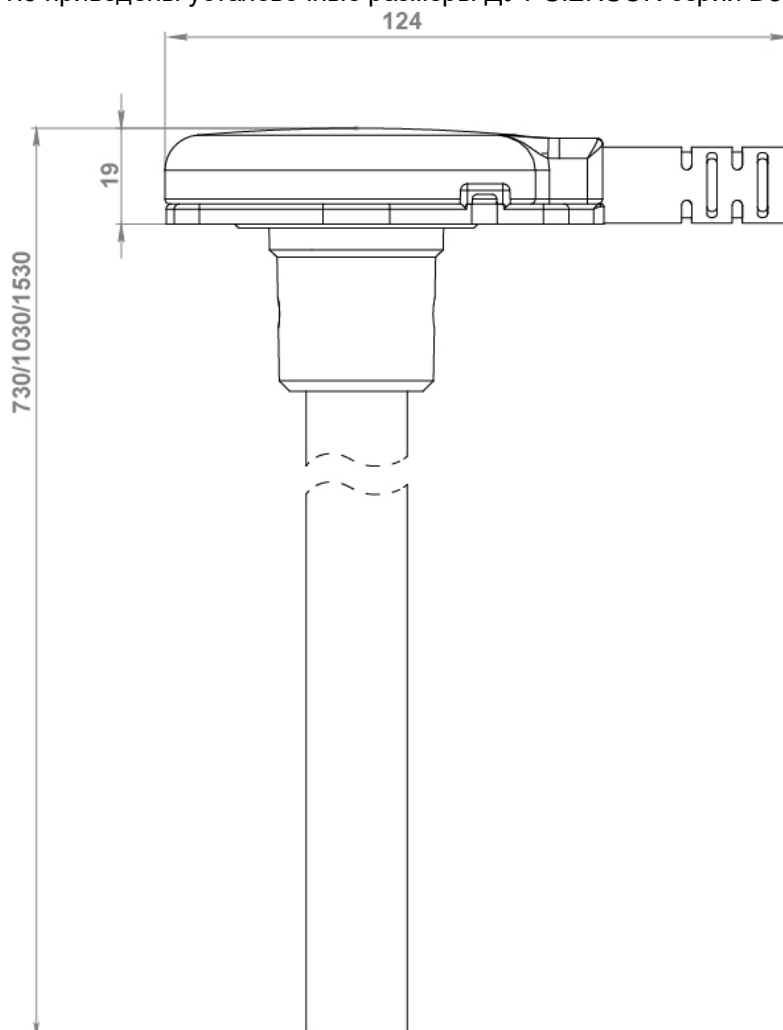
Установочные размеры ДУТ SIENSOR серии D300 – общий вид
